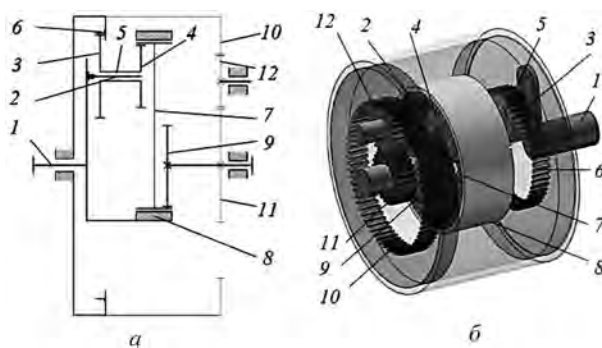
Дифференциально-замкнутый вариатор-редуктор: а – кинематическая схема; б – компьютерная модель; 1 – ведущий вал; 2 – кривошип; 3 – сателлит; 4 – дополнительный зубчатый венец сателлита; 5 – втулка; 6 – центральное зубчатое колесо; 7 – вспомогательный зубчатый венец; 8 – обойма; 9 – выходное зубчатое колесо; 10 – замыкающее зубчатое колесо; 11 – дополнительное выходное зубчатое колесо; 12 – промежуточное зубчатое колесо
